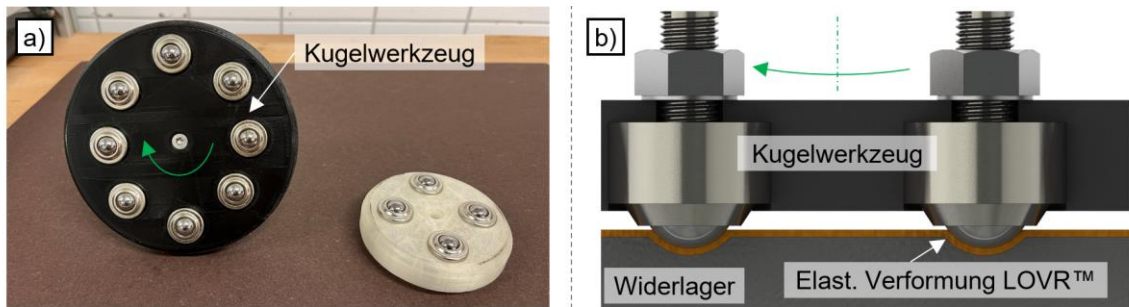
a) Kugelwerkzeuge, b) Wirkprinzip der Flexibilitätssteigerung mit Kugelwerkzeugen.
